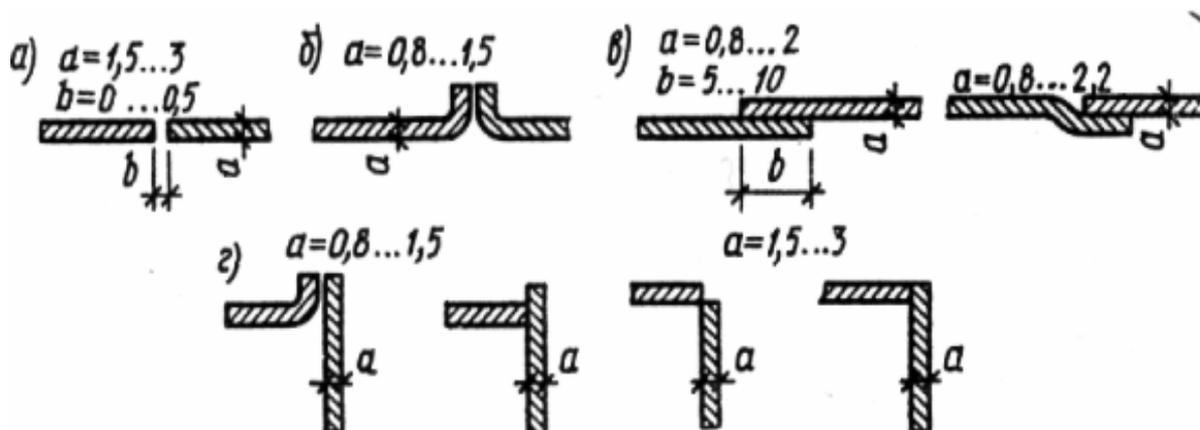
Виды стыковых и нахлесточных сварных соединений.
